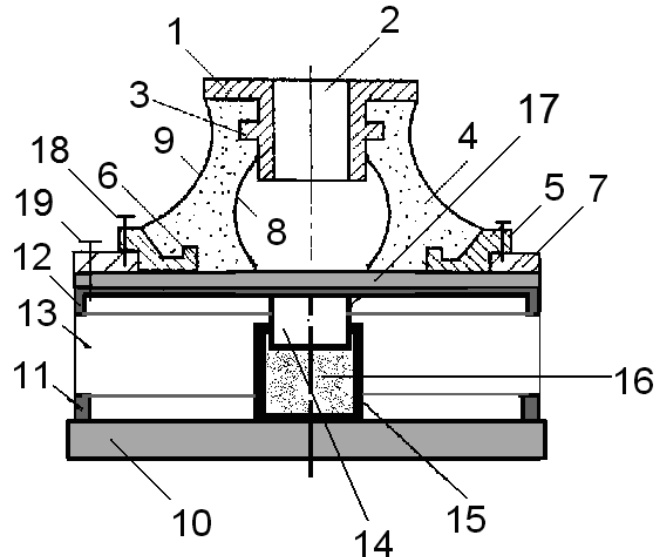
Общий вид резинового виброизолятора с сетчатым демпфером
